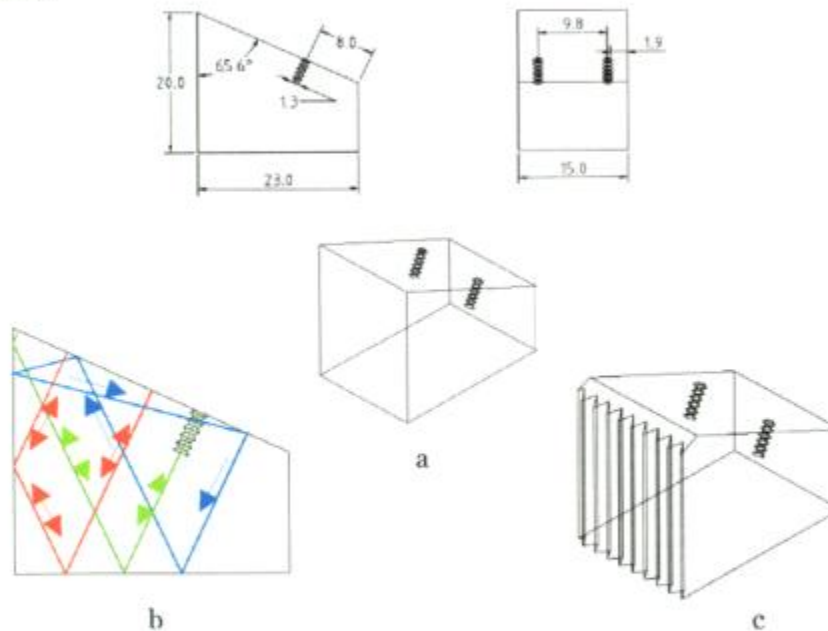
Detalle de la construcción para el transductor MSWS-5: a) dimensiones, b) posibles reflexiones dentro del plástico, c) forma definitiva de la zapata.
